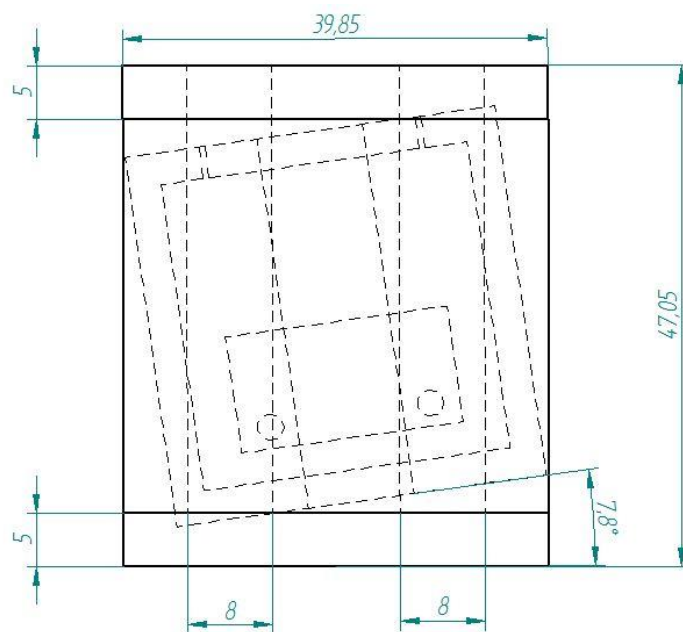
Vista inferior de la base del sensor MMA7341 para montaje en chasis.
